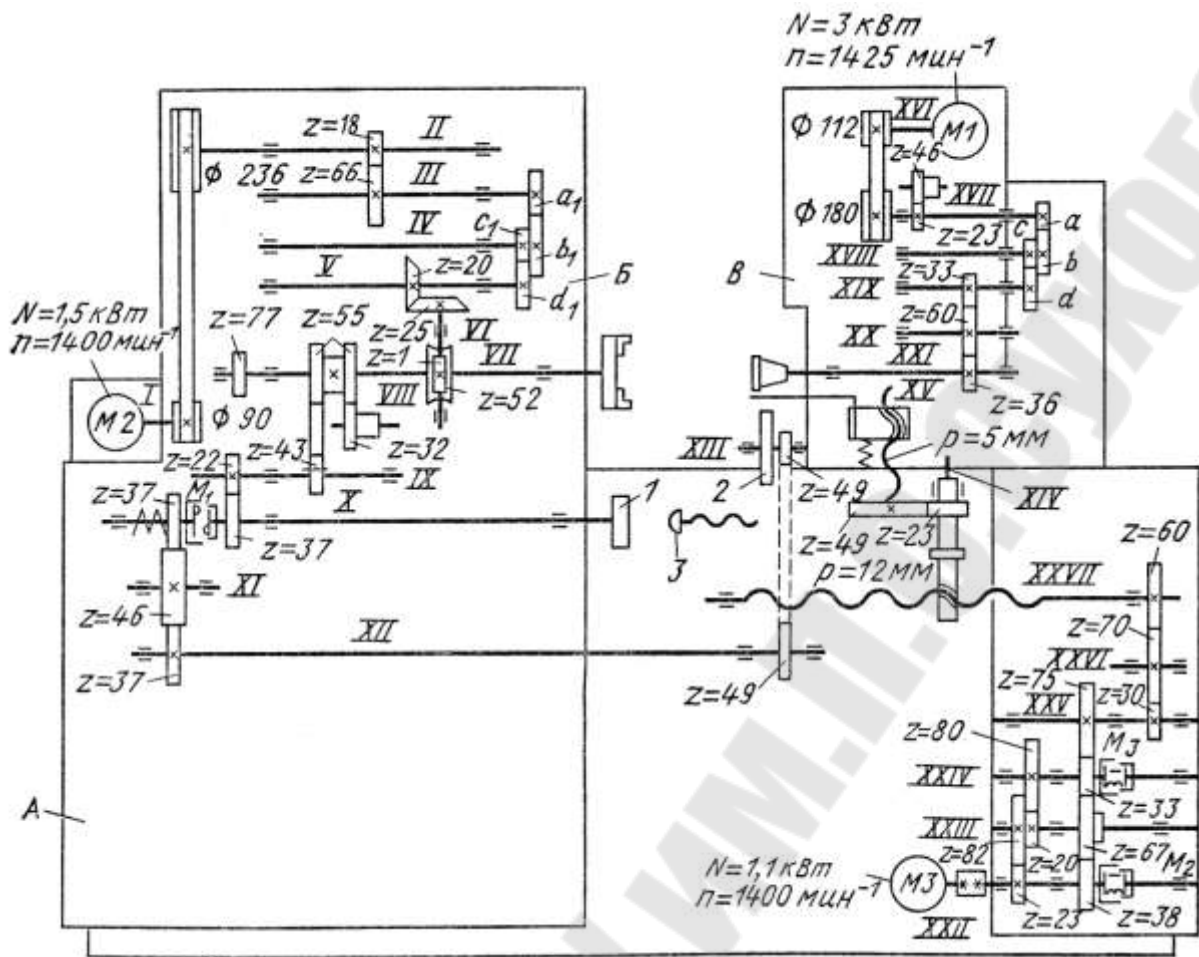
Принципиальная кинематическая схема резьбофрезерного станка модели 5Б63
